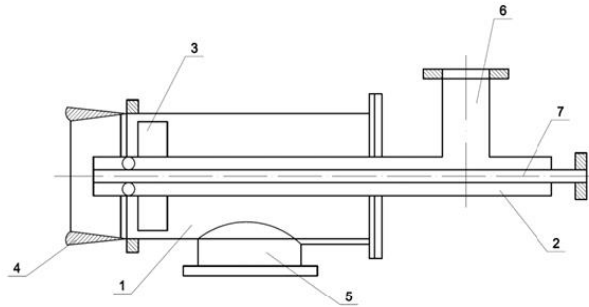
Конструкция газовых горелок: 1 – воздушная камера; 2 – газовая камера; 3 – завихритель; 4 – насадок горелки; 5 – воздушный патрубок; 6 – газовый патрубок; 7 – смотровая труба
